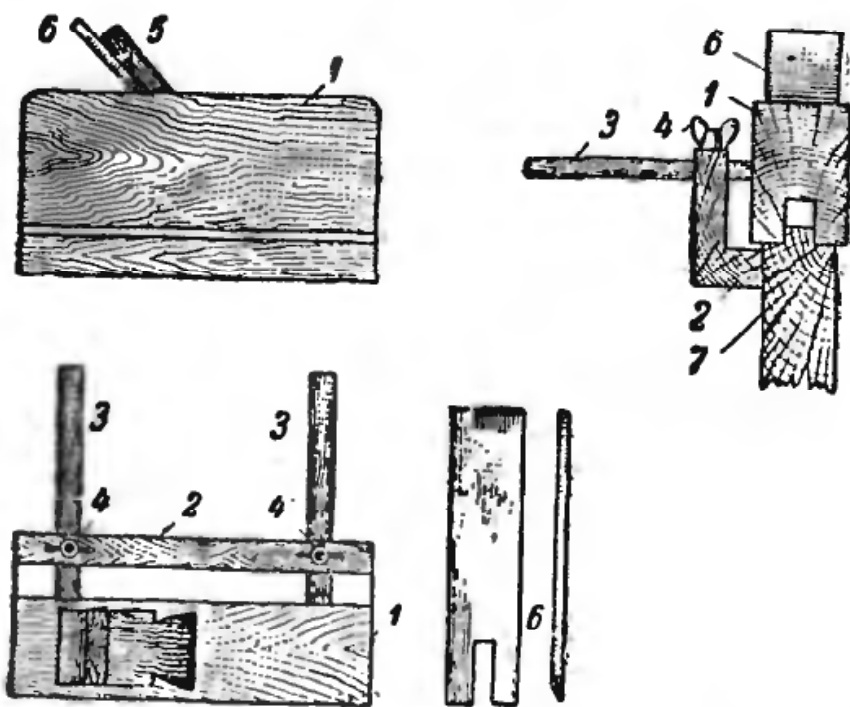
Федергубель: 1 — колодка; 2 — упор (переставная колодка); 3 — направляющие штыри; 4 — стопорные барашки; 5 — клин; 6 — железка; 7 — обрабатываемая деталь.
